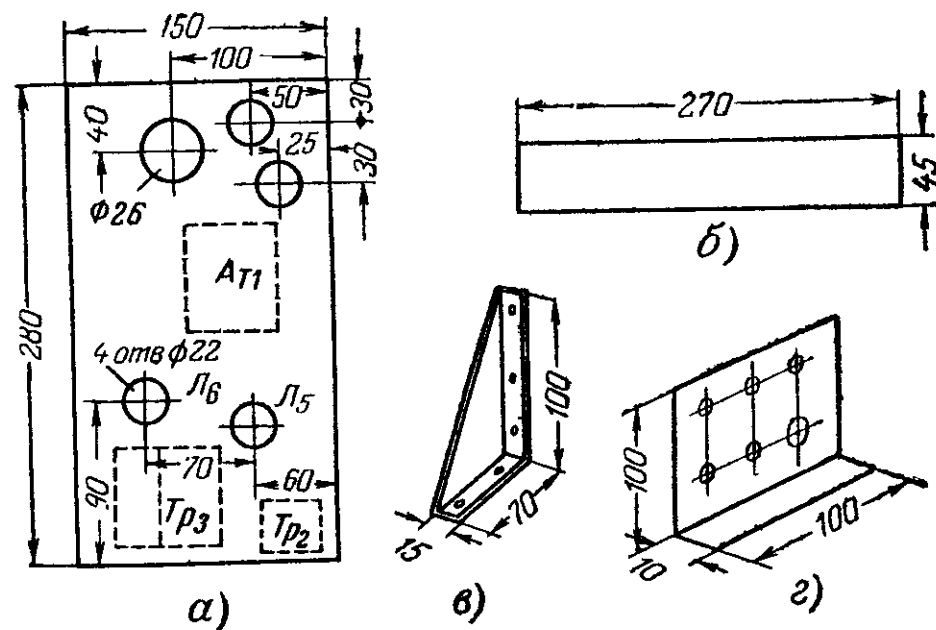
Детали шасси блока развертки для кинескопа 43ЛК9Б.
